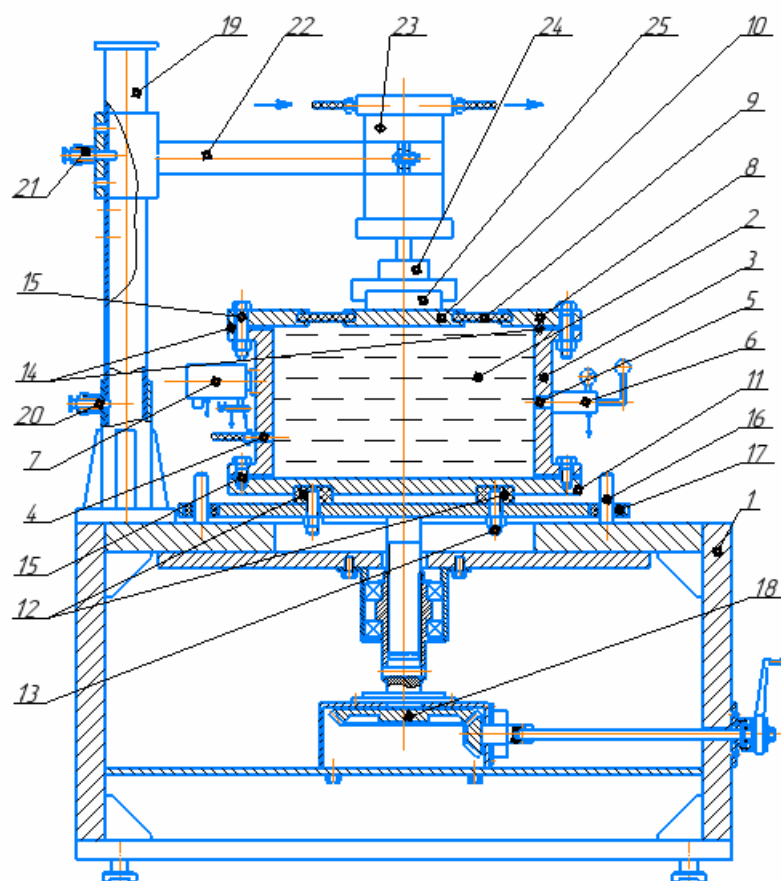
Загальний вид пристрою для притирки плоских поверхонь деталей: 1 – каркас; 2 - робочий стіл; 3 – корпус; 4 - отвори для подачі робочої рідини; 5 - отвір для кріплення дроселя; 6 – дросель; 7 - імпульсний генератор; 8 - верхня кришка; 9 - пружньодемпфуючий елемент плити; 10 - притирочна плита; 11 – нижня кришка; 12 - пружньодемпфуючі елементи; 13 – шпильки; 14 – прокладки; 15 - болтові з'єднання; 16 – напрямні; 17 - пружньодемпфуючі втулки; 18 - механізм підйому; 19 – стійка; 20 - механізм фіксації в горизонтальній площині; 21 - механізм фіксації в вертикальній площині; 22 – важіль; 23 - реверсивний гідромотор; 24 - змінна оправка; 25 - деталь, що притирається
